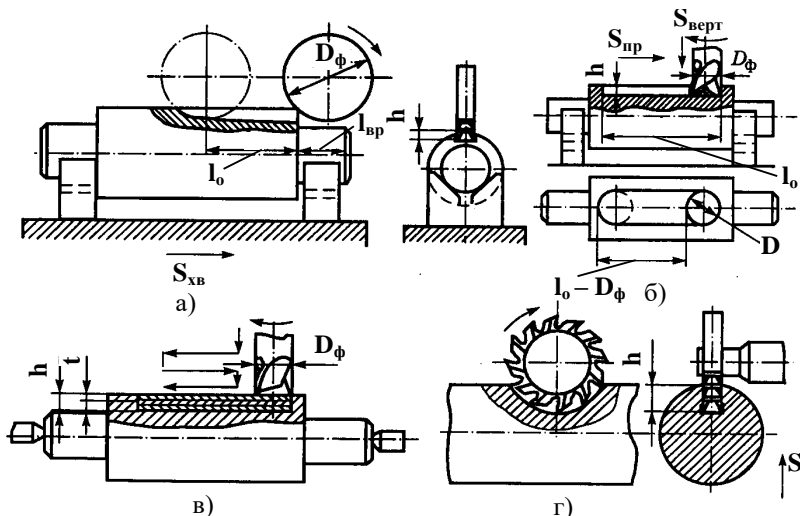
Методи фрезерування шпонкових канавок валів:
